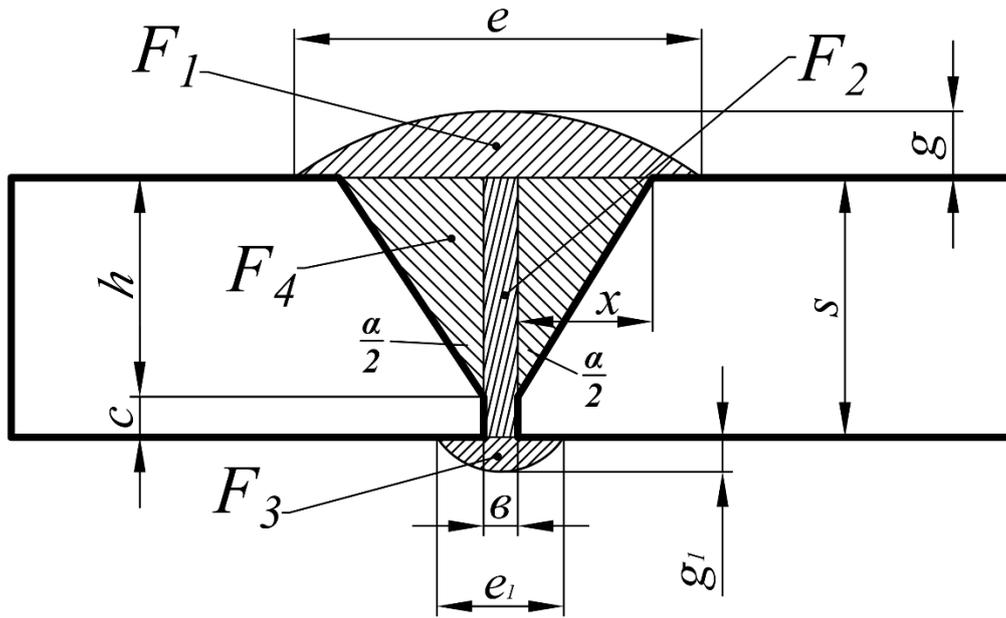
Конструктивні елементи стикового зварного шва С18
